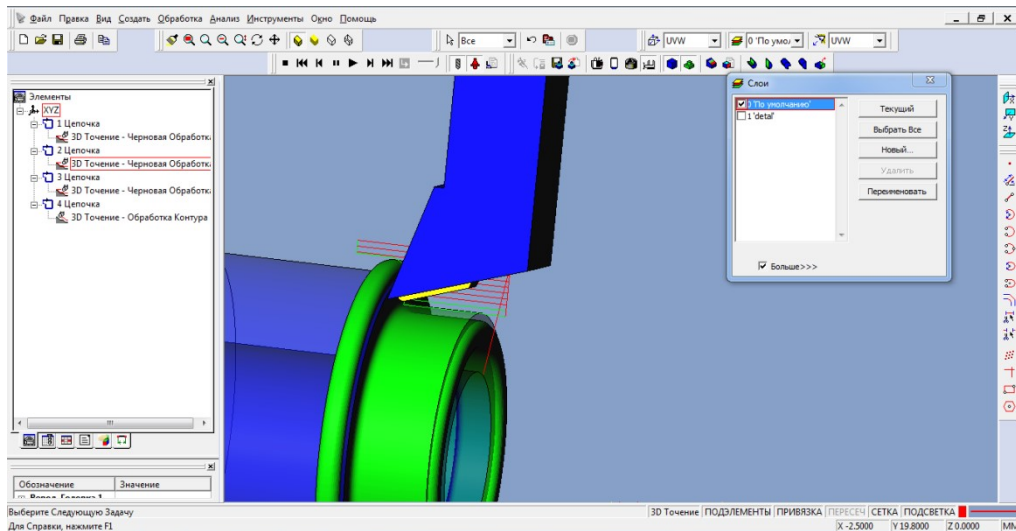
Траектория руху металорізального інструменту при обробленні контуру корпусу
